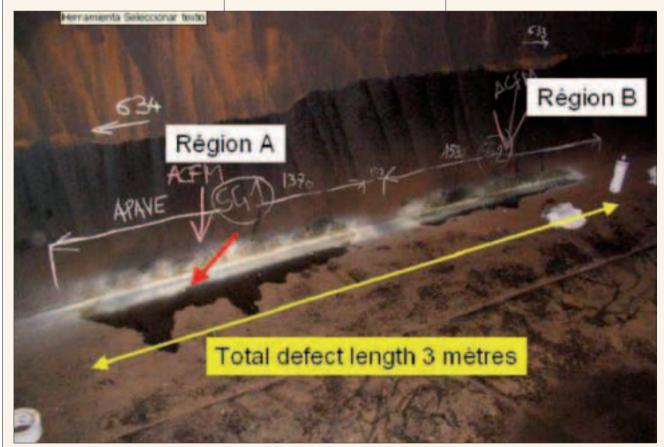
Defecto localizado durante la inspección de un tanque de almacenamiento de combustible
